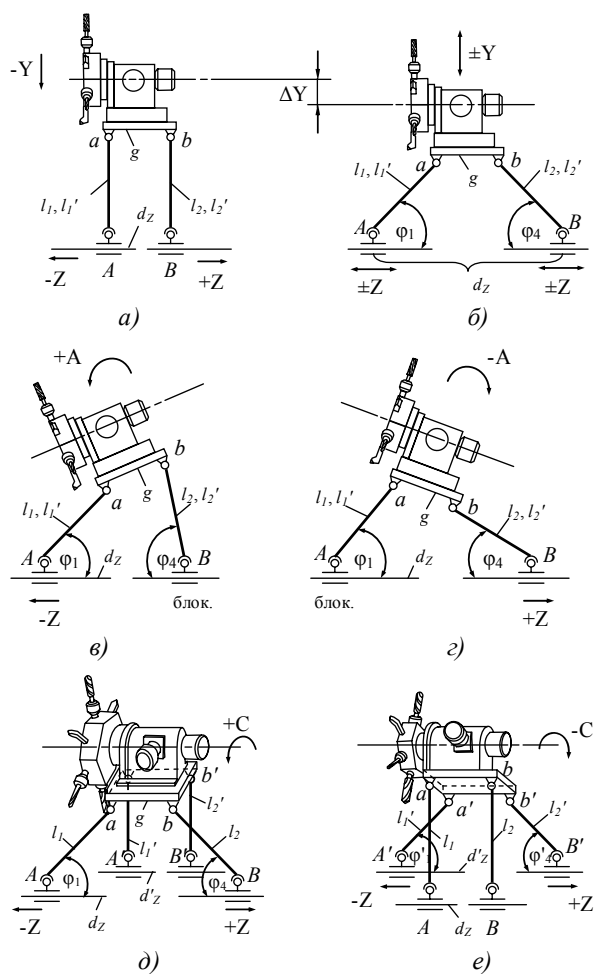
Формообразующие движения инструментальной системы станка по рис.5
